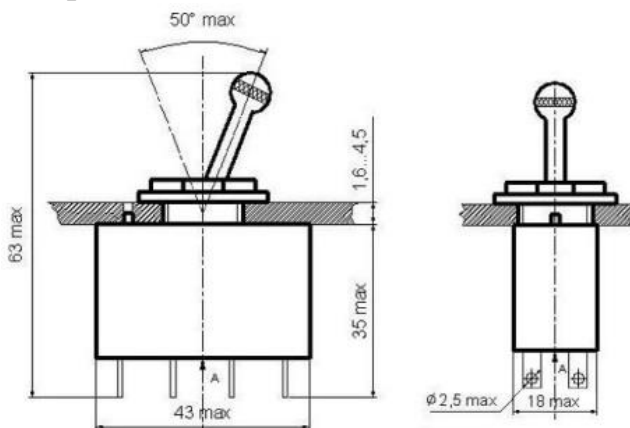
Габаритные и установочные размеры тумблера ТВ 1-4
